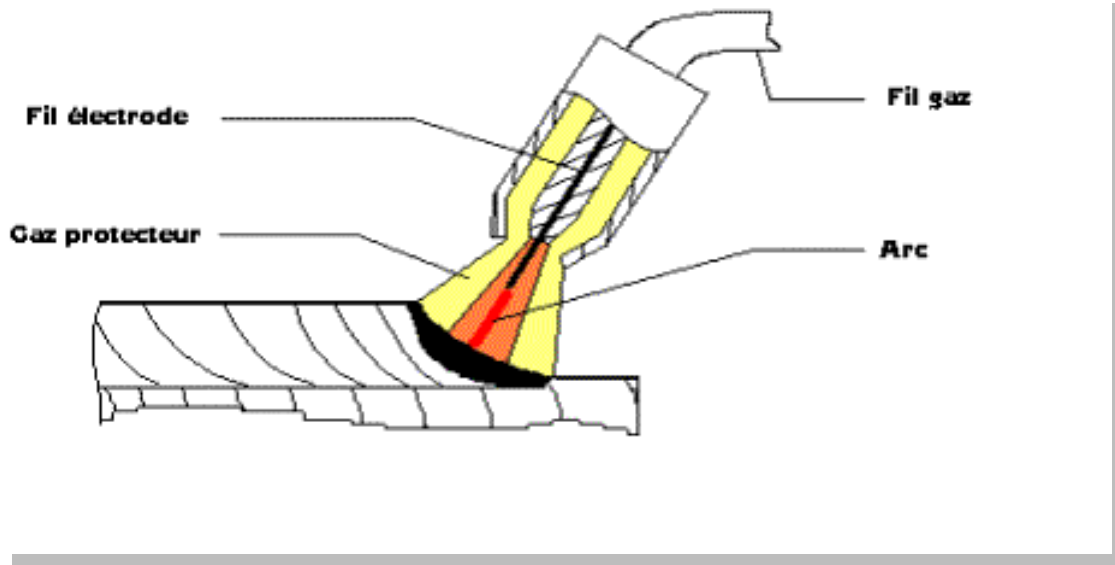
Principe des soudages MIG et MAG.[10].
